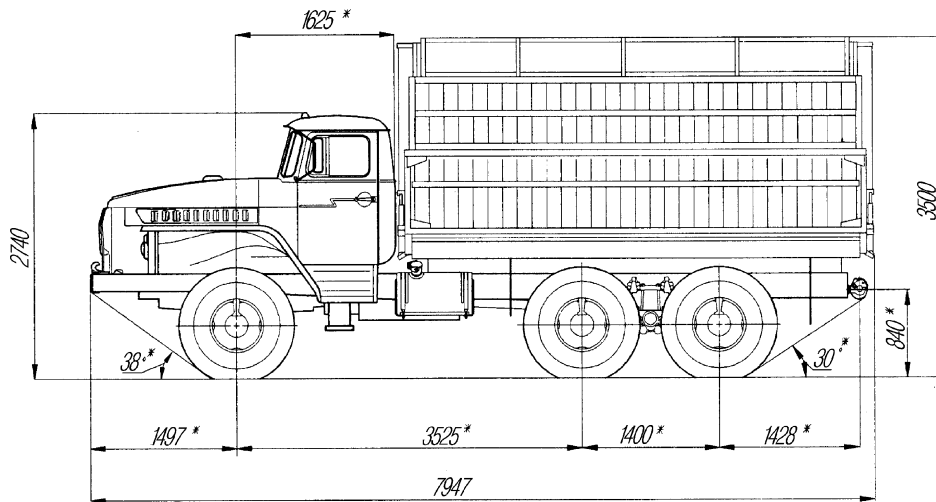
Габаритные размеры автомобиля-самосвала Урал-5557-31
